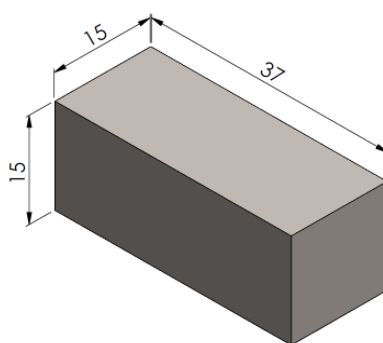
Desenho com dimensões e do corpo de prova de Ti-6Al-4V
